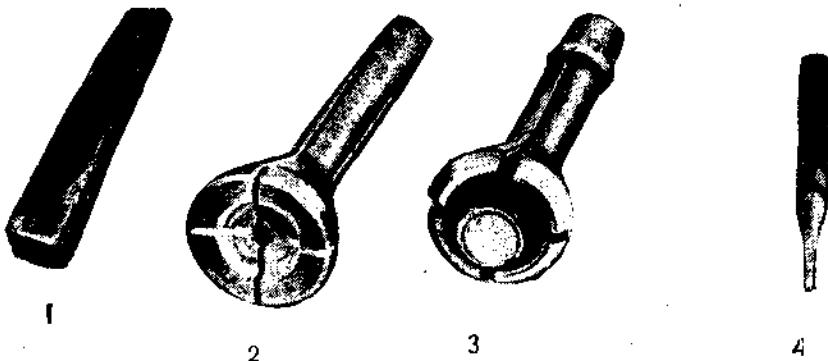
1—Резец для заточки кружков; 2—патрон для заточки; 3—патрон для сверления пуговиц; 4—сверло.
